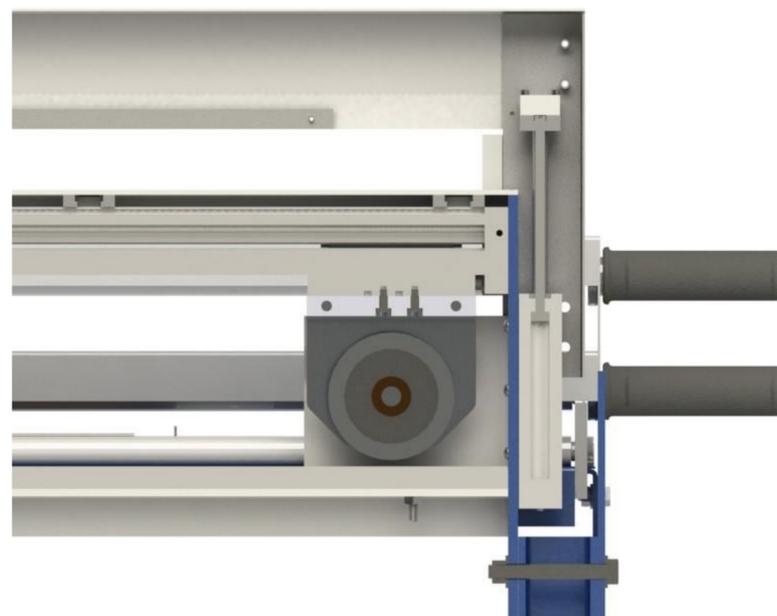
Vue en coupe d’un extrémité de l’assemblage du couteau et du protecteur mobile
